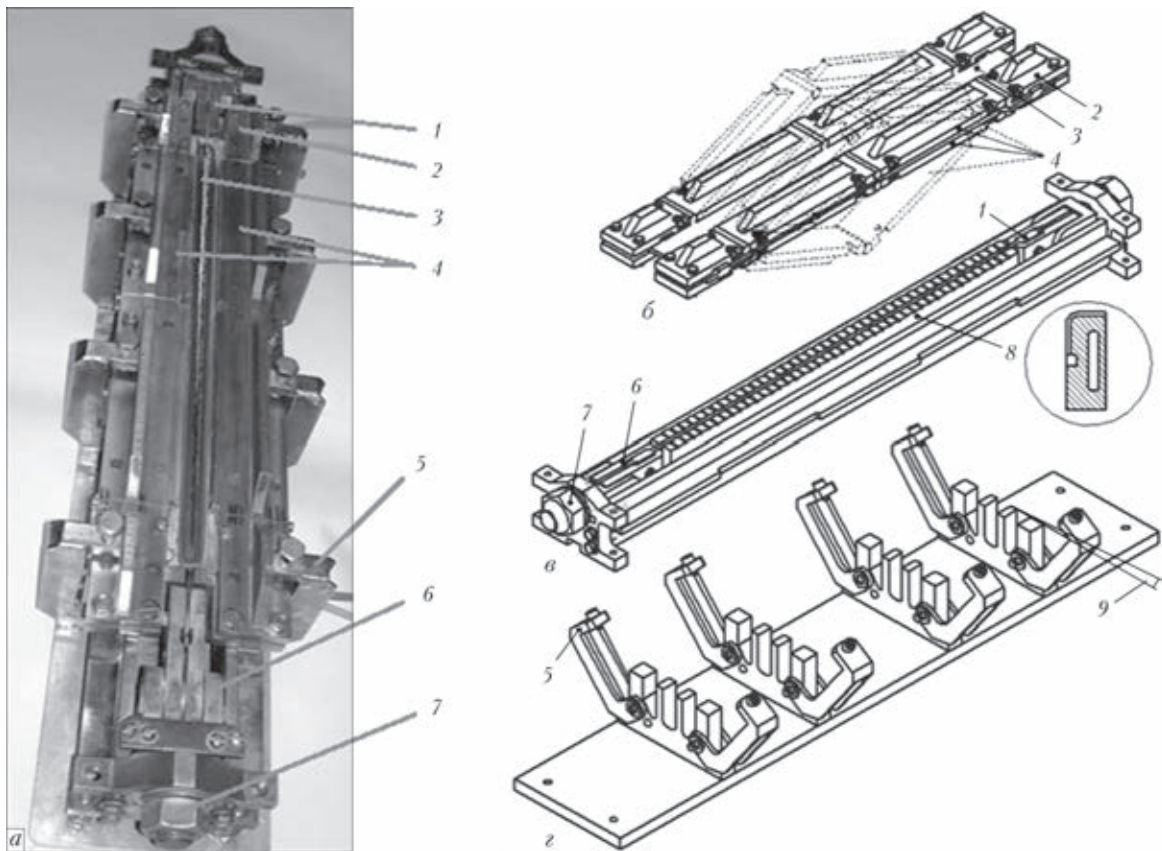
Силовая сборочная оснастка для сварки тавровых образцов в условиях ПУД: *а* — общий вид оснастки с образцом после сварки; *б* — узел растяжения листа; *в* — узел растяжения ребра; *з* — узел стапеля; 1, 2 — захват соответственно ребра и листа; 3 — лист таврового образца; 4 — ломающий рычаг; 5 — прижимы; 6 — тяга домкрата; 7 — гайка домкрата; 8 — медная водоохлаждаемая подкладка; 9 — угол поперечного изгиба листа
